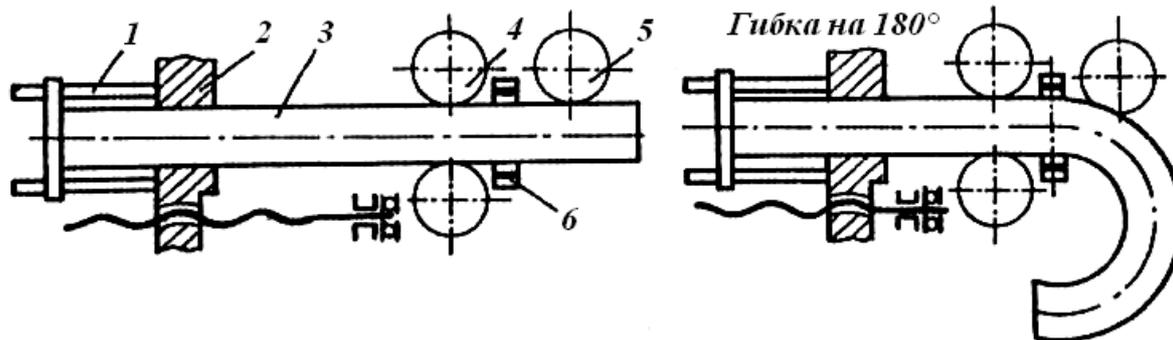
Схема трубогибочного станка с индукционным подогревом:
